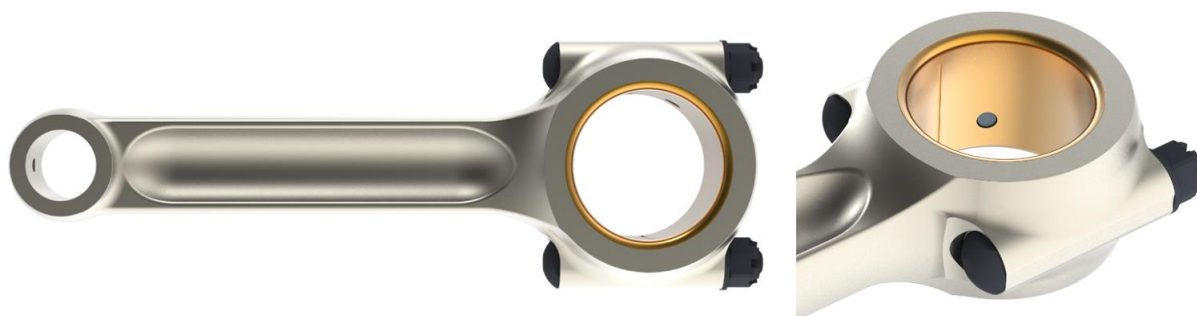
Ojnice motoru Mikron III C; b) detail hlavy ojnice
